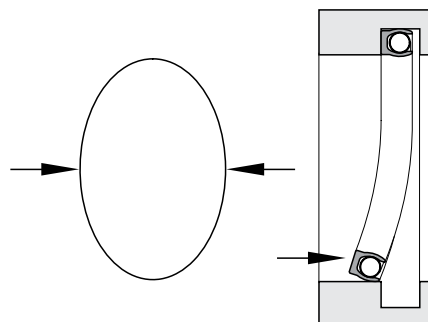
Установка закрытой посадочной канавки в режиме штока
